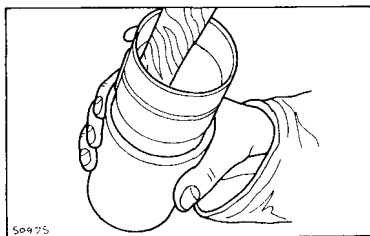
Устанавливать поршни следует с помощью специального приспособления для сжатия колец, загоняя их в цилиндр ручкой молотка
